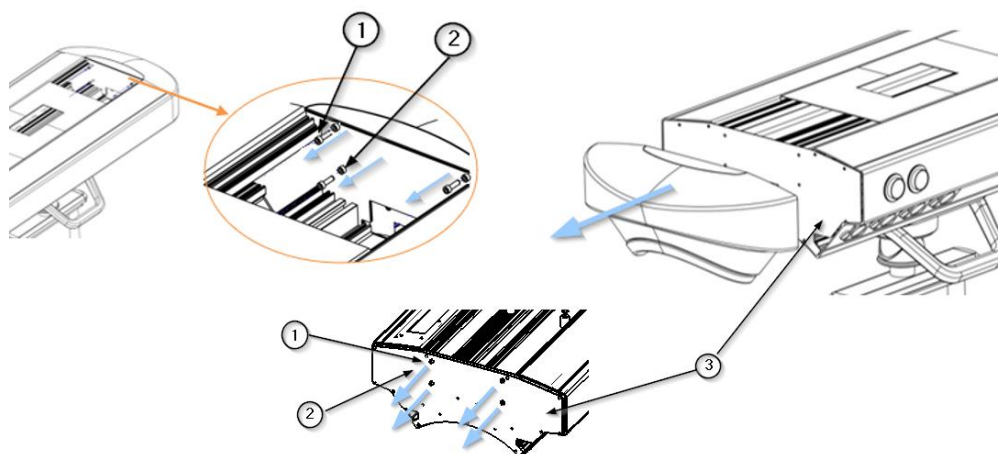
Démontage/assemblage des embouts sur le corps principal d'ABITUS
